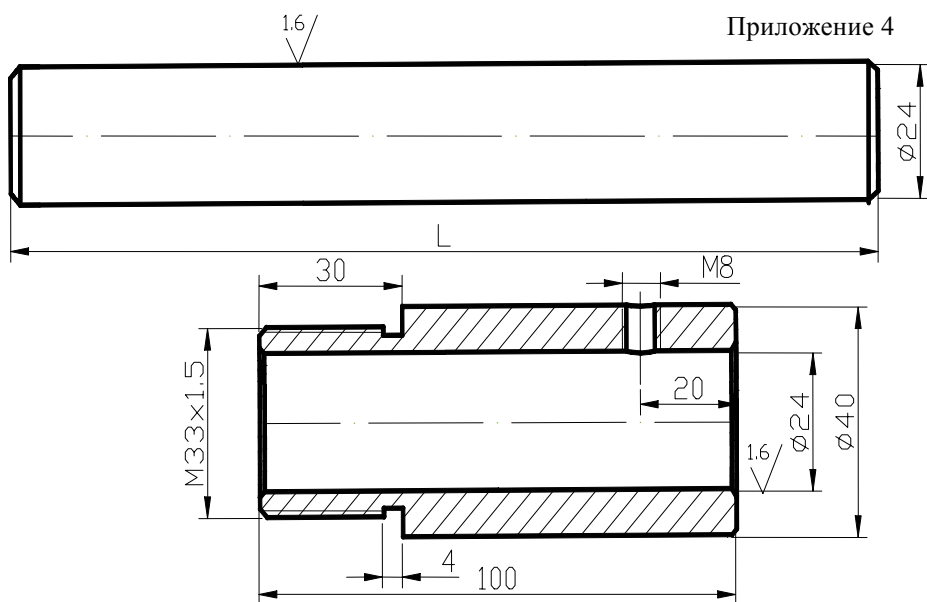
Штанга и втулка для монтажа гнезд ПЭП на трубопроводе.
